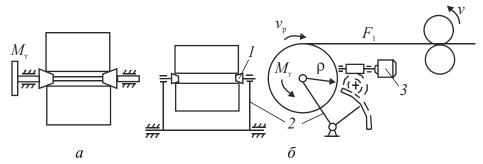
Схемы рулонных установок: a — шпиндельная установка; δ — бесшпиндельная установка: I — консольный вал; 2 — поворотный рычаг; 3 — электродвигатель
